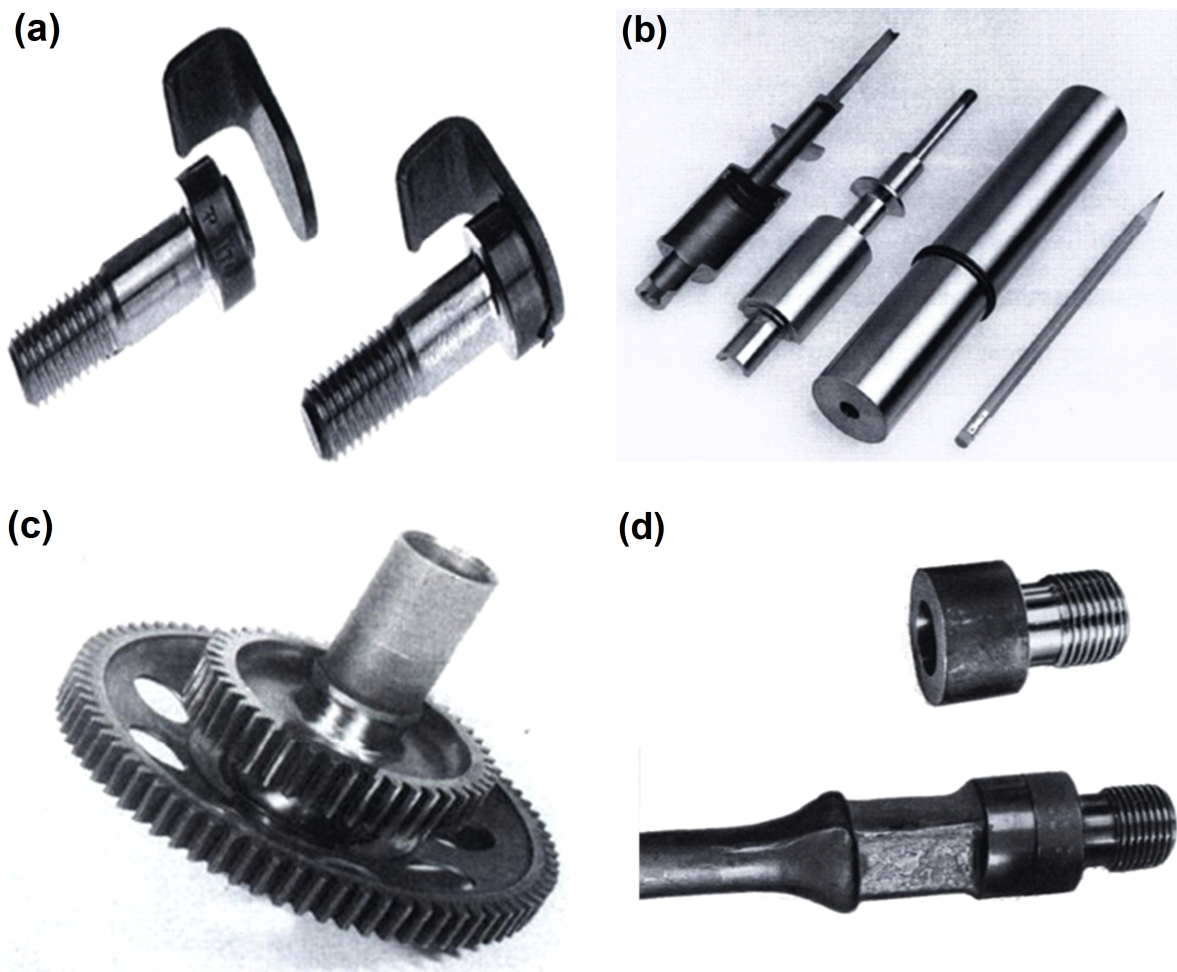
Quelques applications industrielles du soudage par friction rotative [6].
